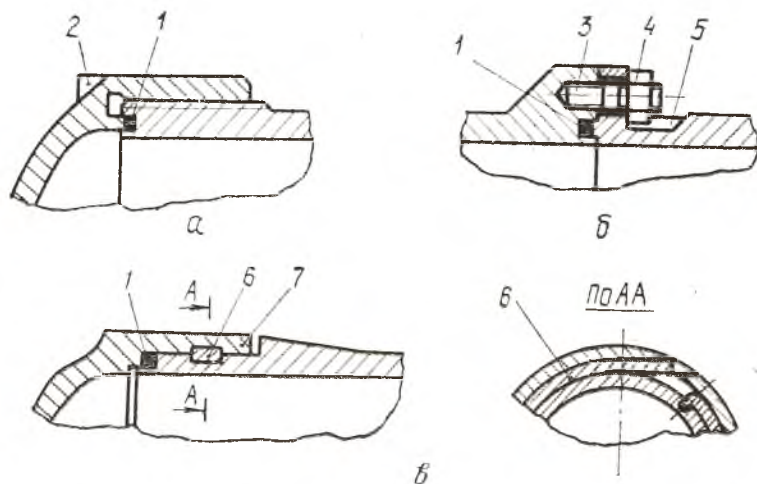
Конструкция соединений: а — резьбового; б — фланцевого; в — шпоночного: 1 — уплотнительное кольцо; 2 — выступы под ключ; 3 — шпилька; 4 — гайка; 5 — углубление в стенке под ключ; 6 — шпонка; 7 — обойма
